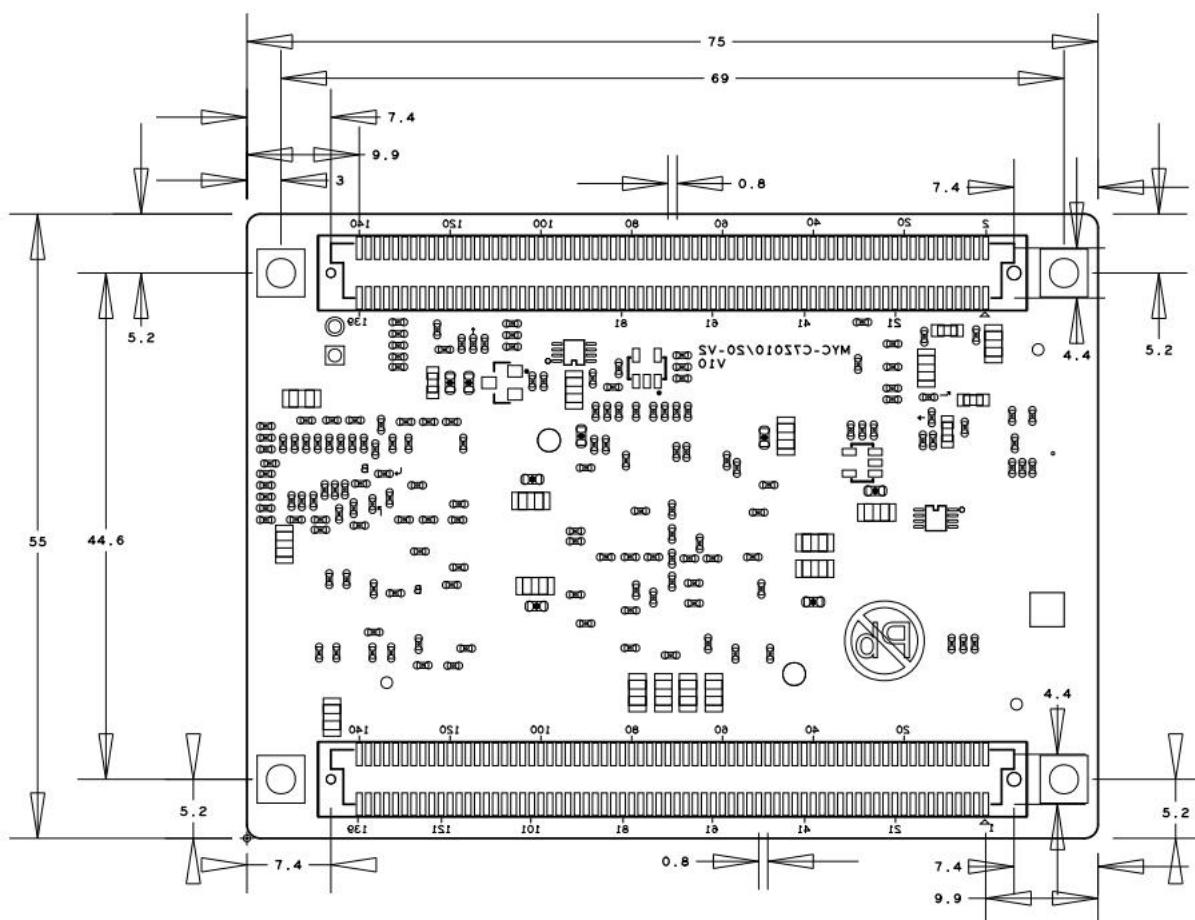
MYC-C7Z010-20-V2-核心板 PCB 封装(单位: mm)
